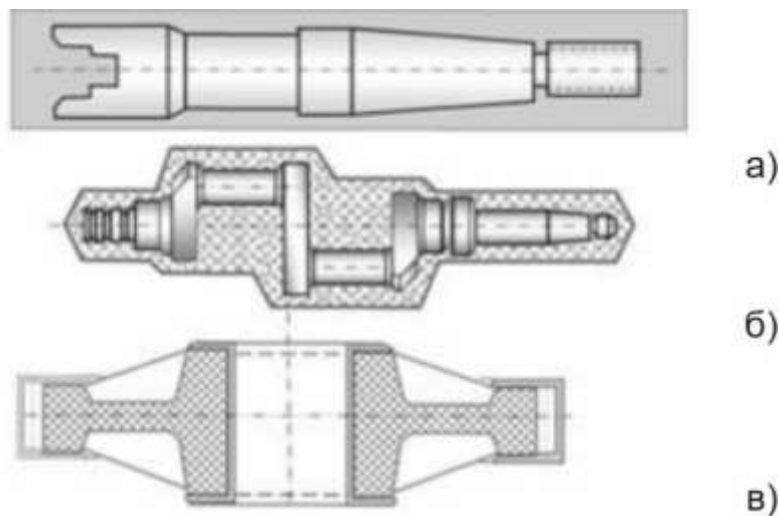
Заготовки деталей: а-прокат, б-поковка, в – виливок.
